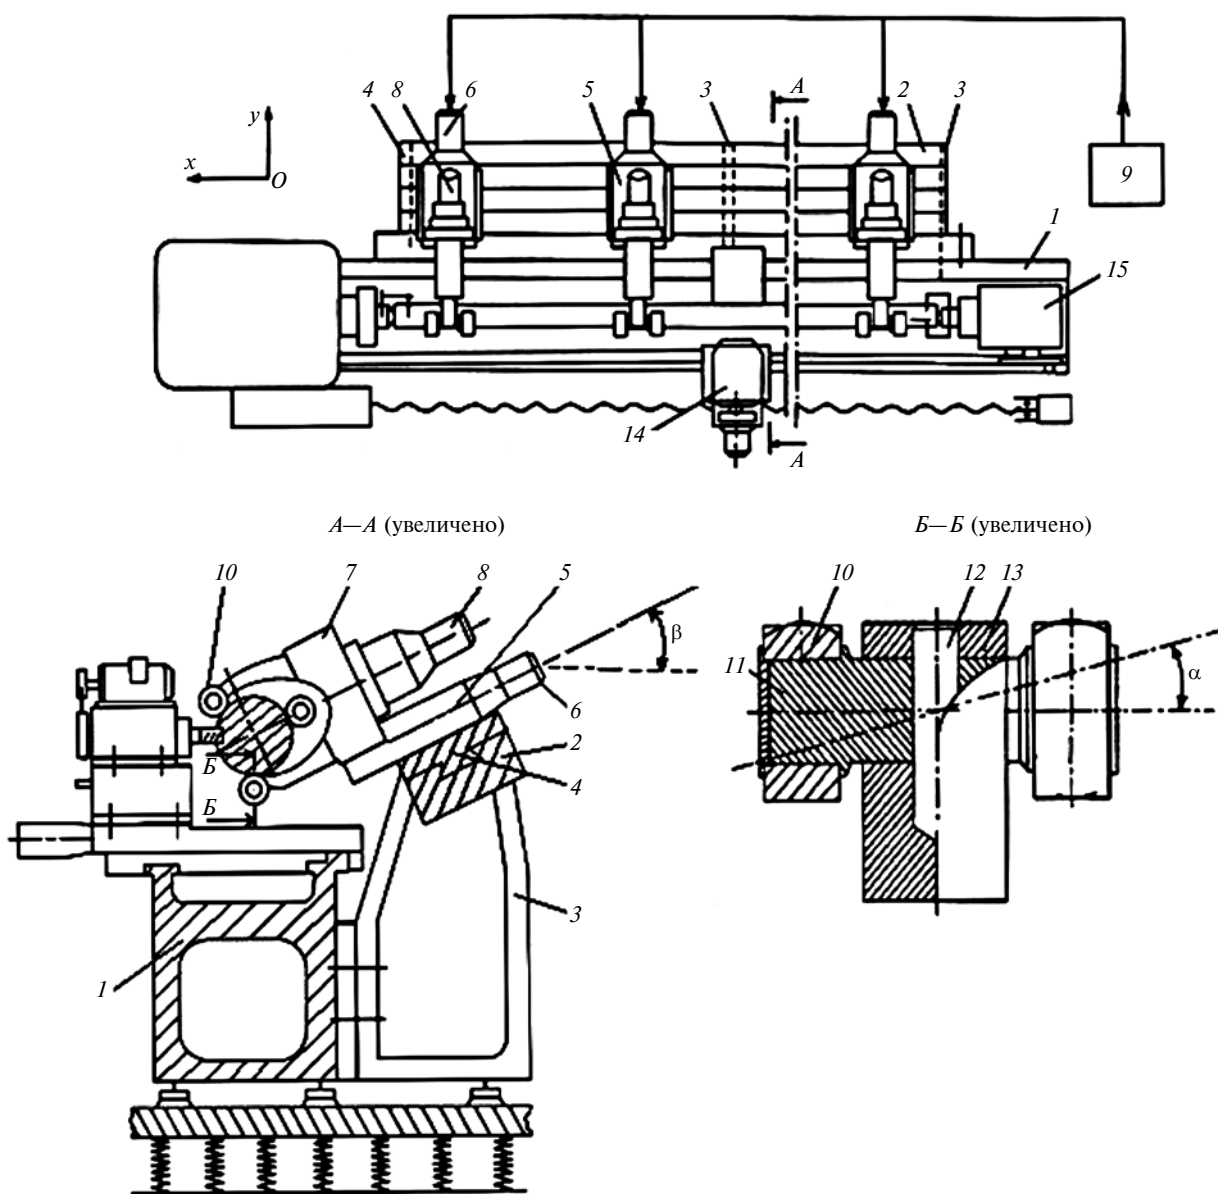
Установка для точения и фрезерования шпоночных пазов длинномерных осесимметричных деталей
